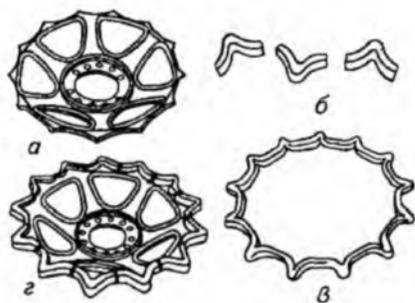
Схемы восстановления ведущего колеса приваркой секторов:
